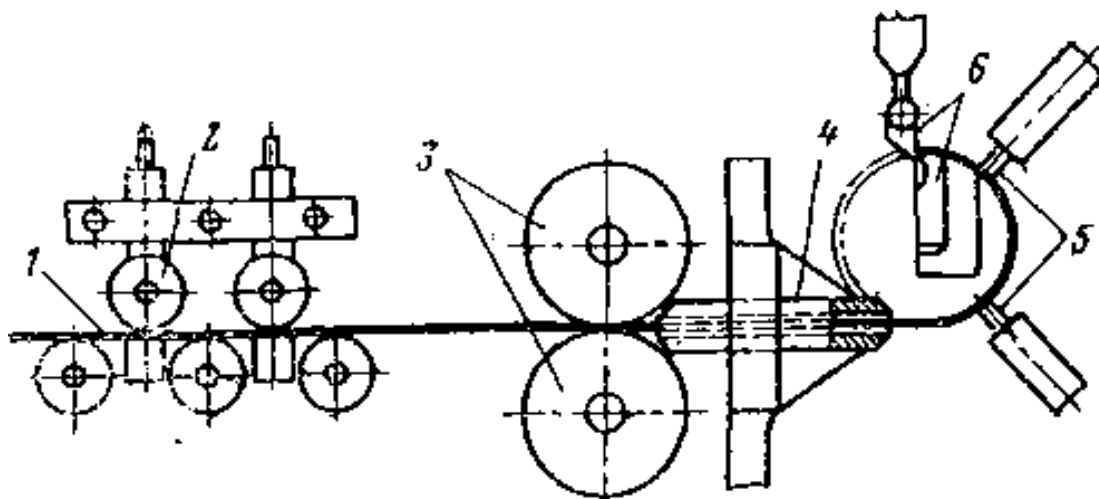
Схема безоправочного навивання пружини на пружинонавивальному автоматі
